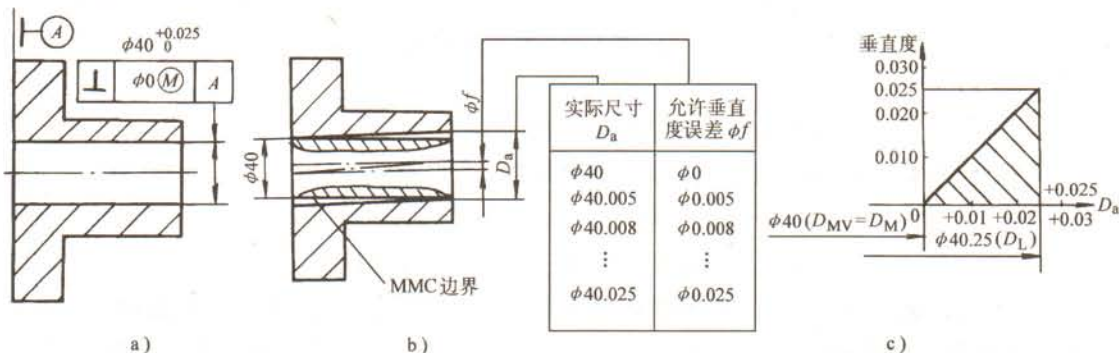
关联要素采用最大实体要求的零形位公差标注
